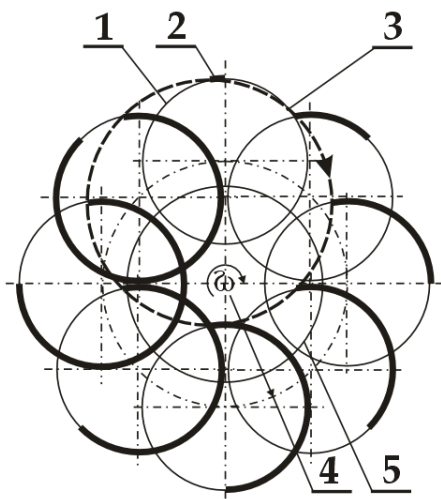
Кинематическая схема нанесения наплавочного металлопокрытия по технологии «The Gleason Process»: 1 – контур профиля шатунной шейки коленчатого вала; 2 – зона горения дуги и формирования наплавочного валика; 3 – траектория движения зоны горения дуги; 4 – радиус кривошипа; 5 – контур профиля коренной шейки коленчатого вала [9, 12]
